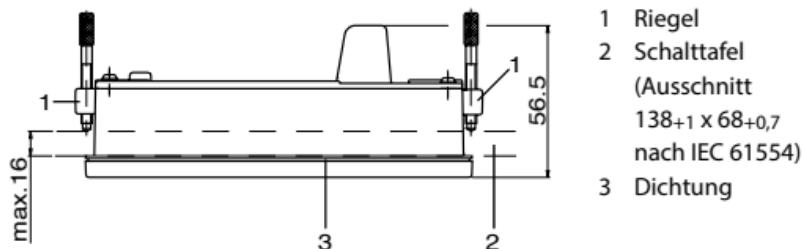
Draufsicht – Einbau in Schalttafel
